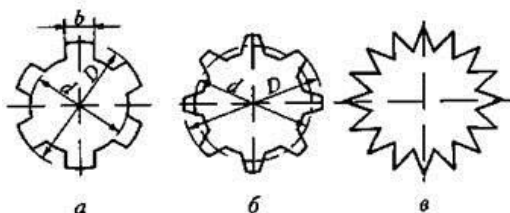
Форма поперечного сечения выступов зубчатых соединений: прямобоочные, эвольвентные, треугольные
